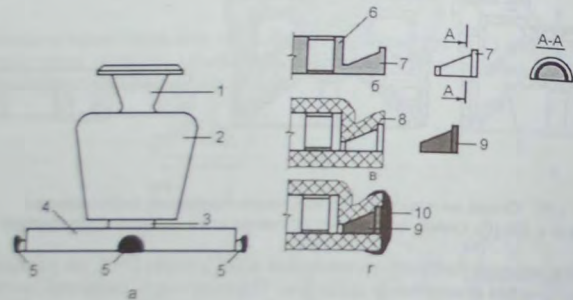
Схема установки промывников в КО: 1 — ЛВ; 2 — верхняя прибыль; 3 — шейка прибыли; 4 — отливка; 5 — промывники; 6 — бандаж модели отливки; 7 — модель промывника; 8 — КО; 9 — керамическая пробка; 10 — самотвердеющая огнеупорная смесь
